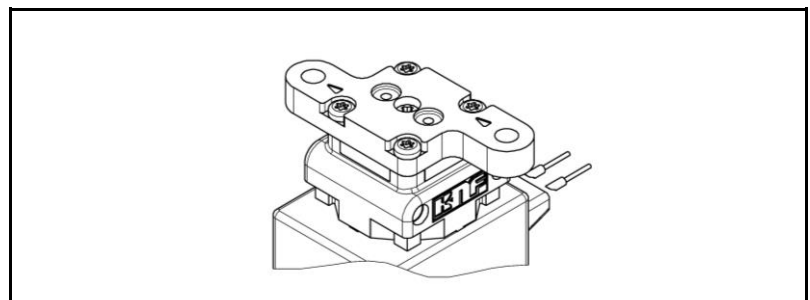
Pumpenkopf mit Flanschbefestigungs-Anschluss
